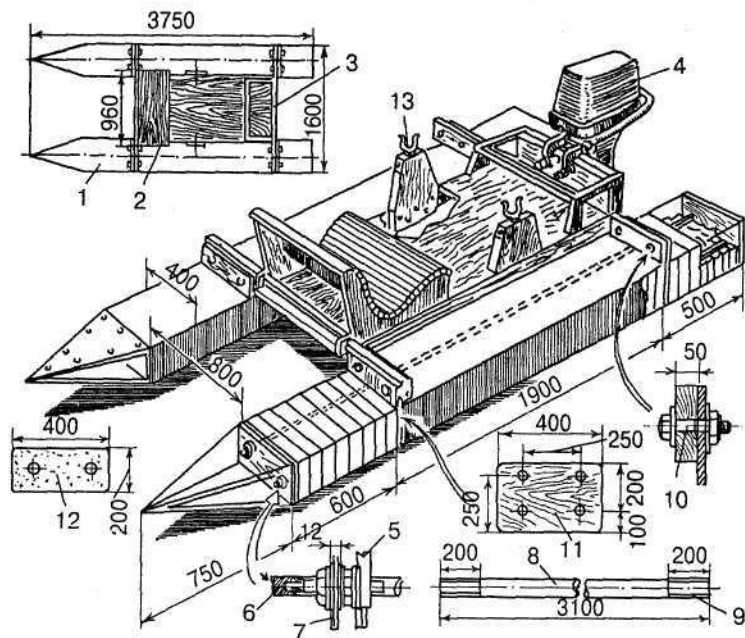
Катамаран с поплавками из пенопласта: 1 — поплавок; 2 — сиденье; 3 — подмоторная рама; 4 — мотор 1,5-3 л.с.; 5 — перегородка; 6 — пробка; 7 — диафрагма; 8 — стяжка; 9 — резьба трубная 1/2"; 10 — болт М10; 11 — шпангоут; 12 — пенопласт-пластины толщ. 50 мм; 13 — уключина
